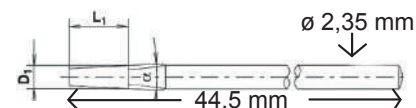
Confezione: 6 pz / packaging: 6 pieces / emballage: 6 pièces
